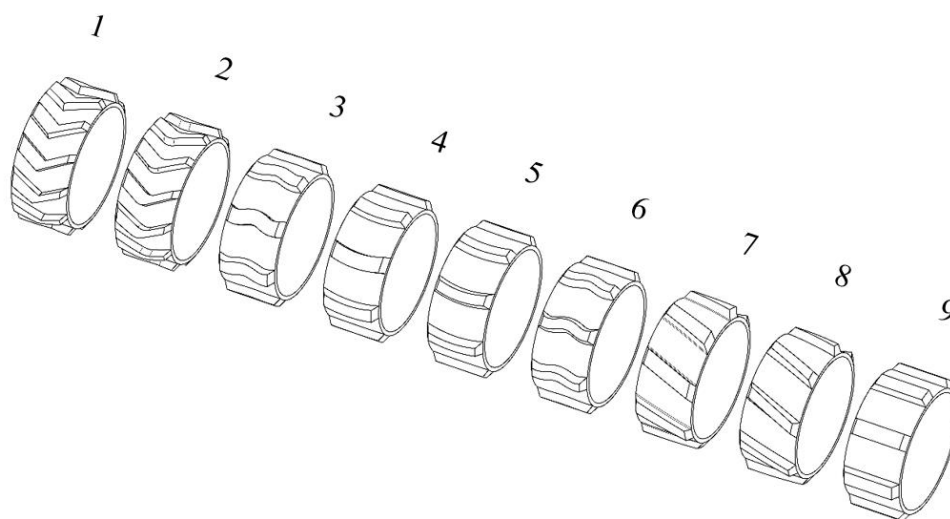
Эскизы вариантов профилей лопастей вращающегося колеса центратора
